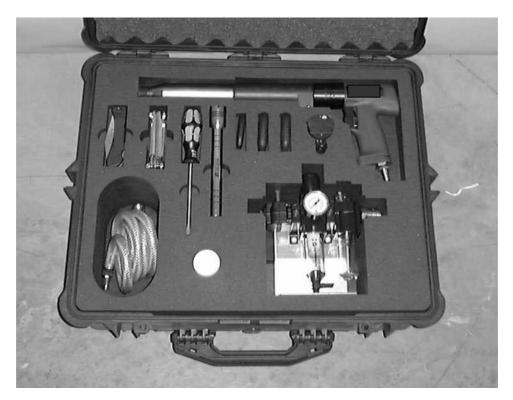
Вид контейнера станка VM2150S с пневматическим приводом
